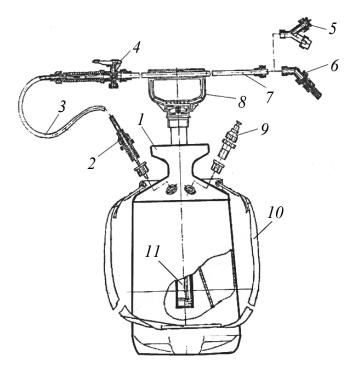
Опрыскиватель РЖ-12: I — бак; 2 — штуцер; 3 — шланг; 4 — запорный кран; 5 — двойная форсунка; 6 — одинарная форсунка; 7 — штанга брандспойта; 8 — ручка штока насоса подкачки воздуха; 9 — предохранительный клапан;
